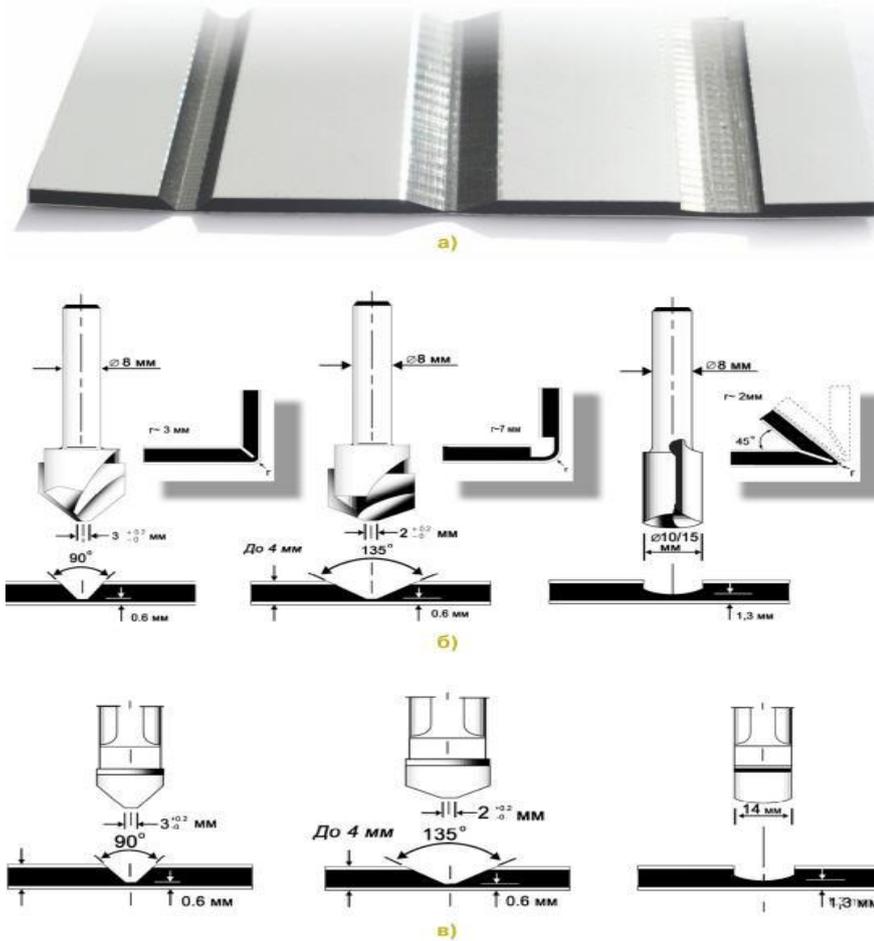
Фрезеровка пазов: а) виды пазов; б) профиль паза пальчиковых фрез; в) профиль паза дисковых фрез
